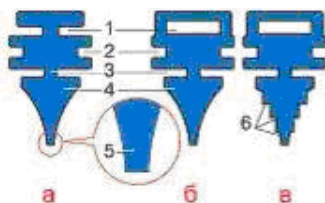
Профили лент щеток стеклоочистителя: 1 – пазы для упругих пластин; 2 – пазы для зажимов каркаса; 3 – шейка; 4 – рабочая часть; 5 – рабочая кромка; 6 – острые кромки на боковых поверхностях рабочей части; *а* – профиль ленты для щетки с двумя упругими пластинами; *б* – профиль ленты для щетки с одной упругой пластиной; *в* – профиль ленты с острыми кромками на боковых поверхностях рабочей части
